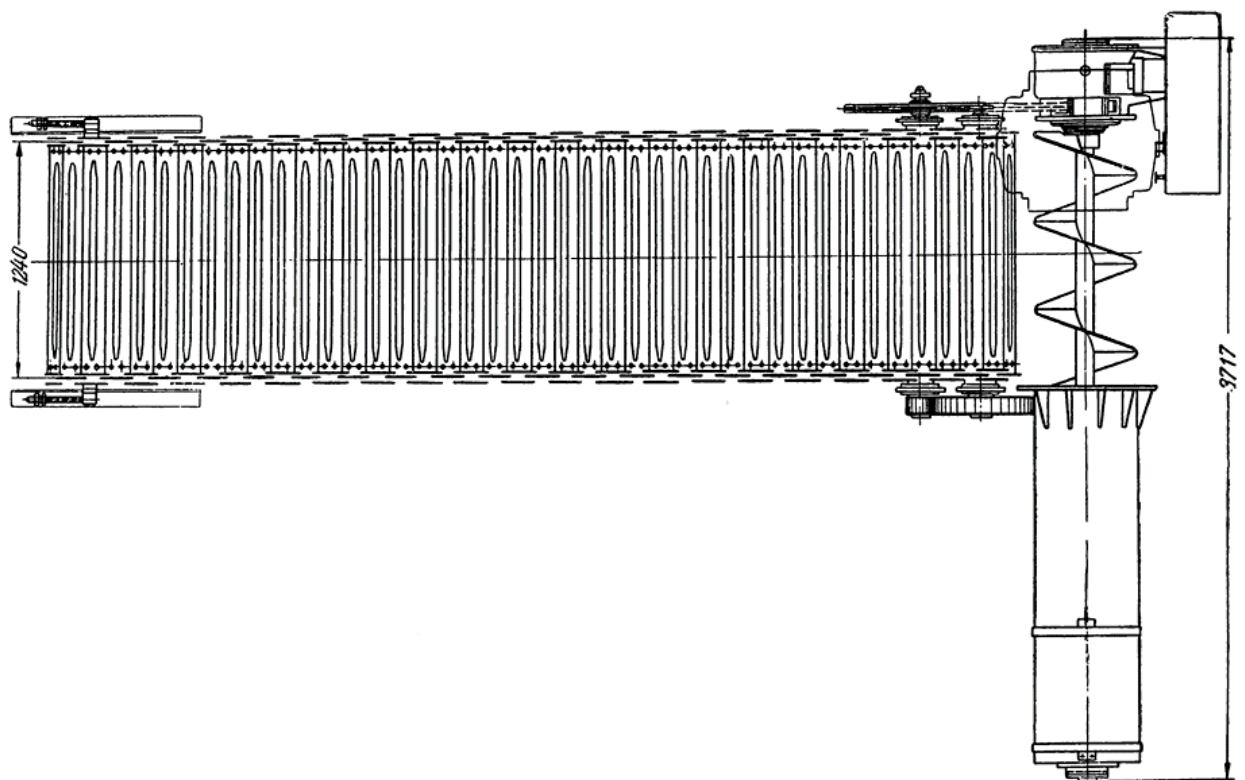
Подвижное дно и шнековый пресс стилочной машины
